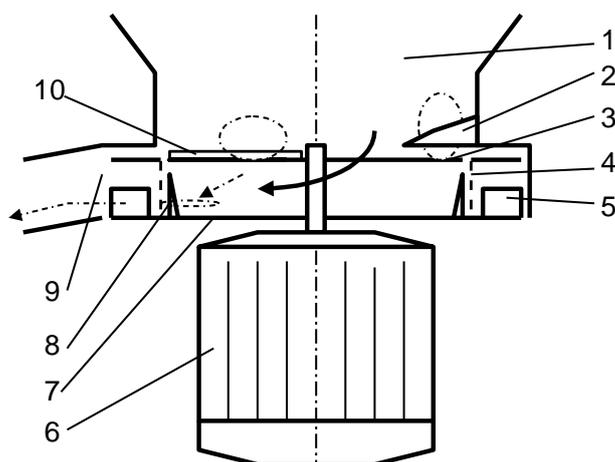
Корнерезка-пастоизготовитель КПИ-4:
